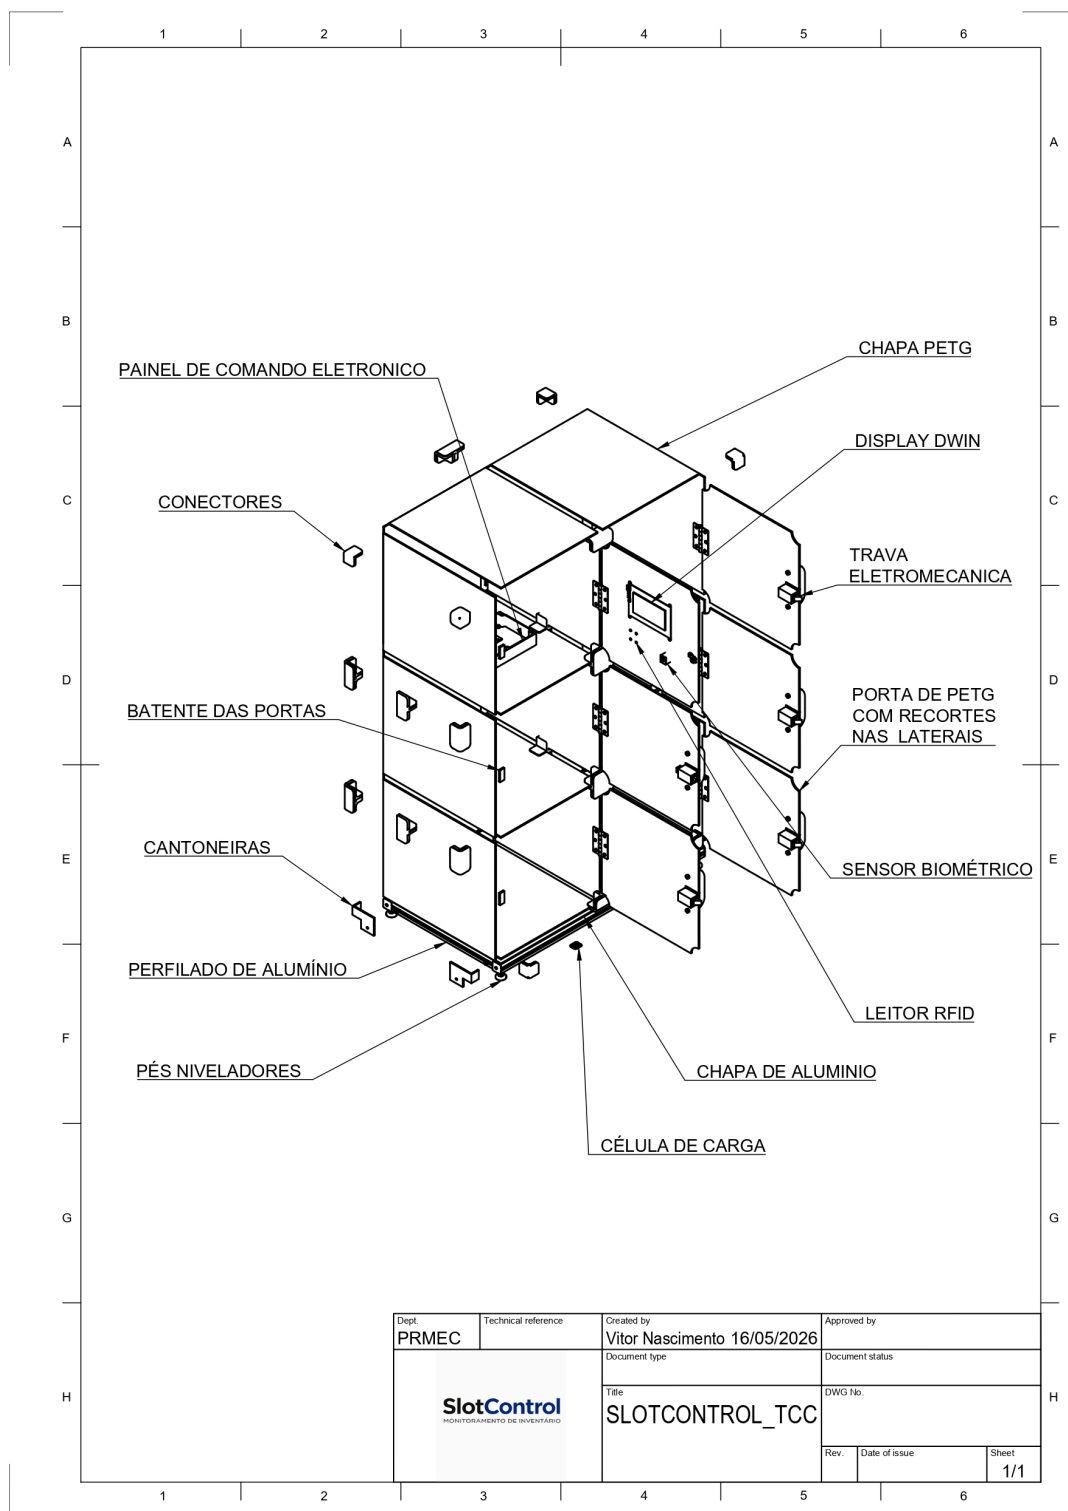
Desenho técnico explodido da VRP com identificação dos componentes principais.
